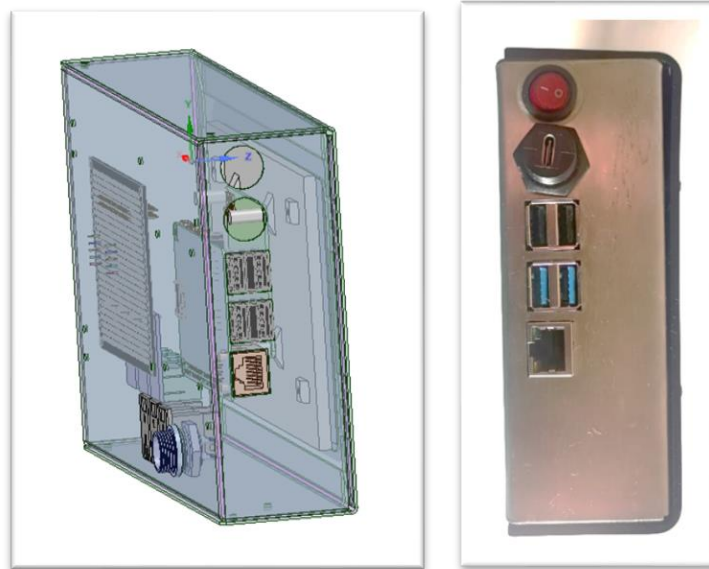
Diseño y ensamble de la caja del módulo lateral
